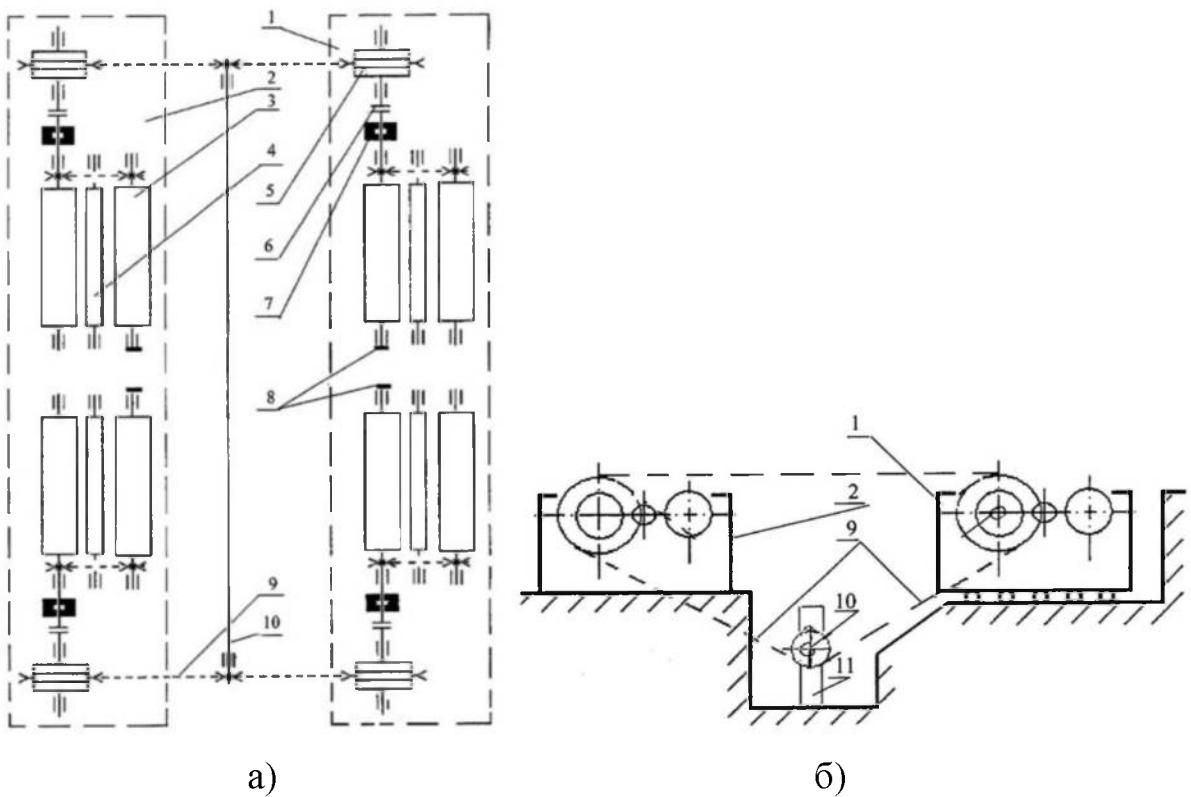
Схема устройства по патенту РФ №2276026
